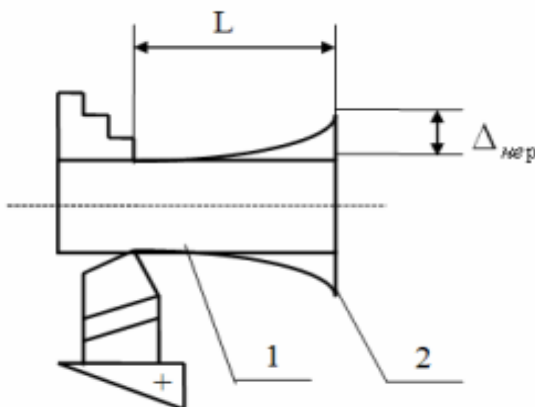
Схема погрешности формы обрабатываемой детали
